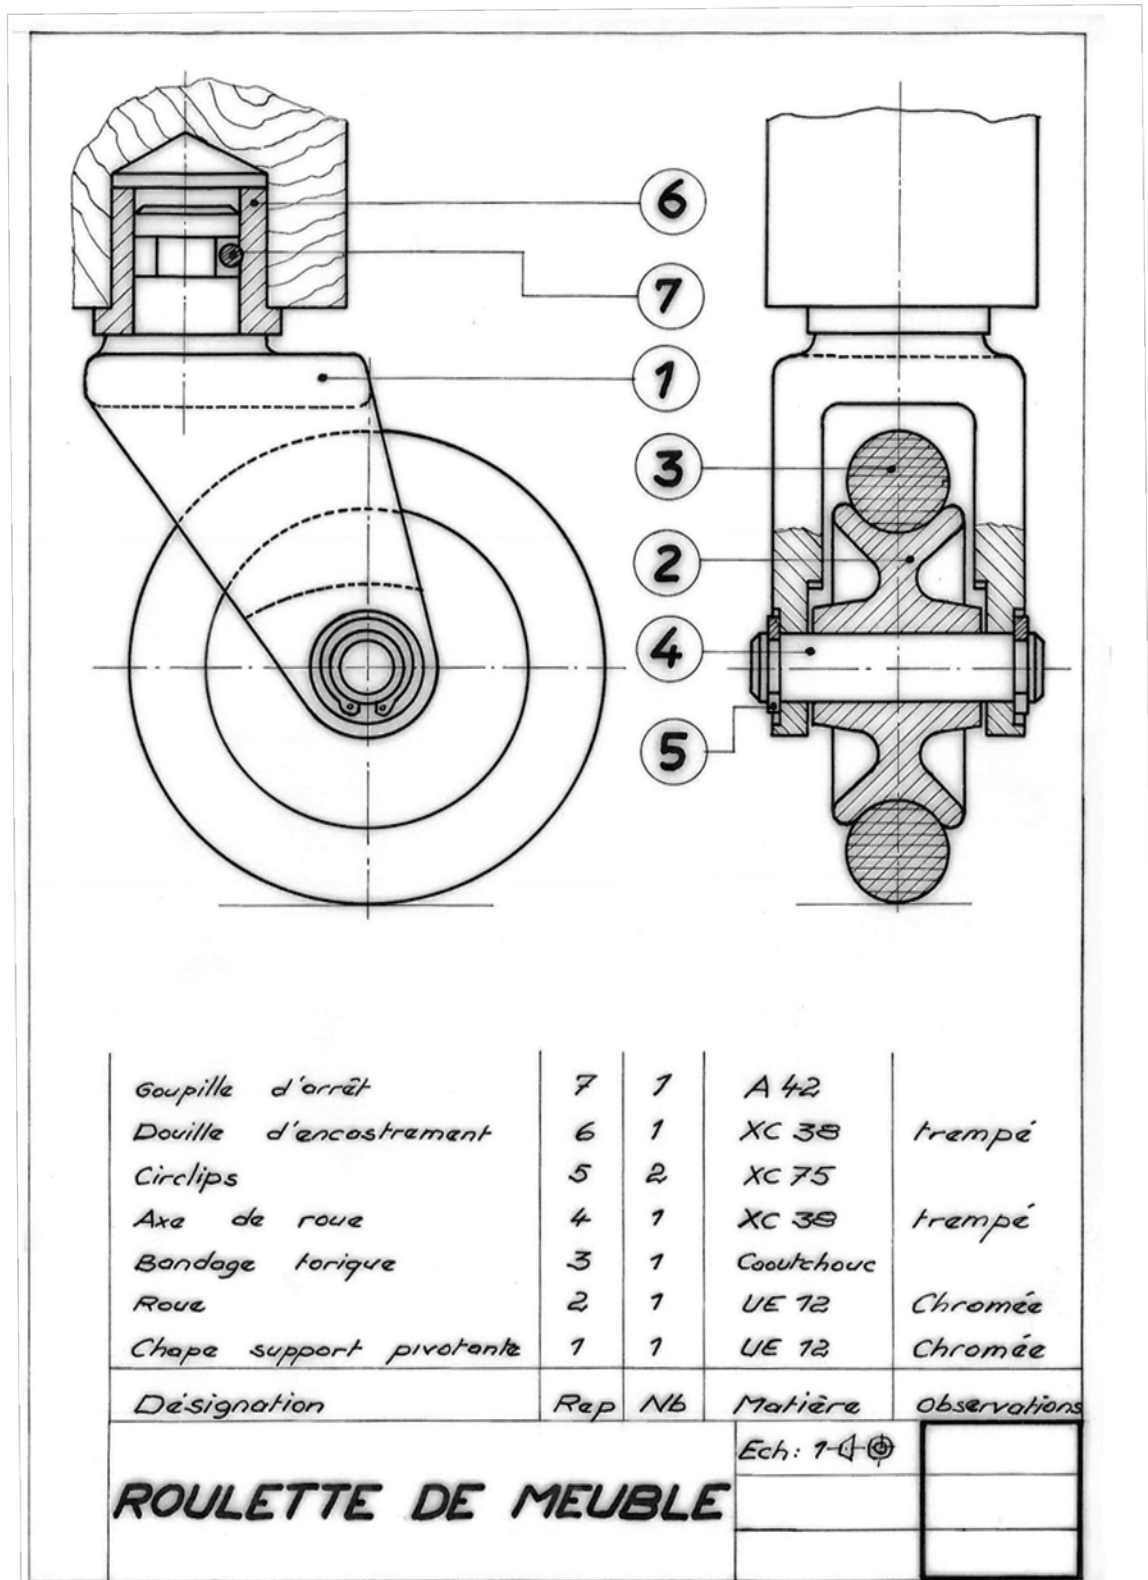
Exemple d'un dessin d'ensemble de Roulette de meuble
